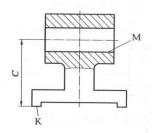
Эскиз обрабатываемой детали к заданию 1.32
